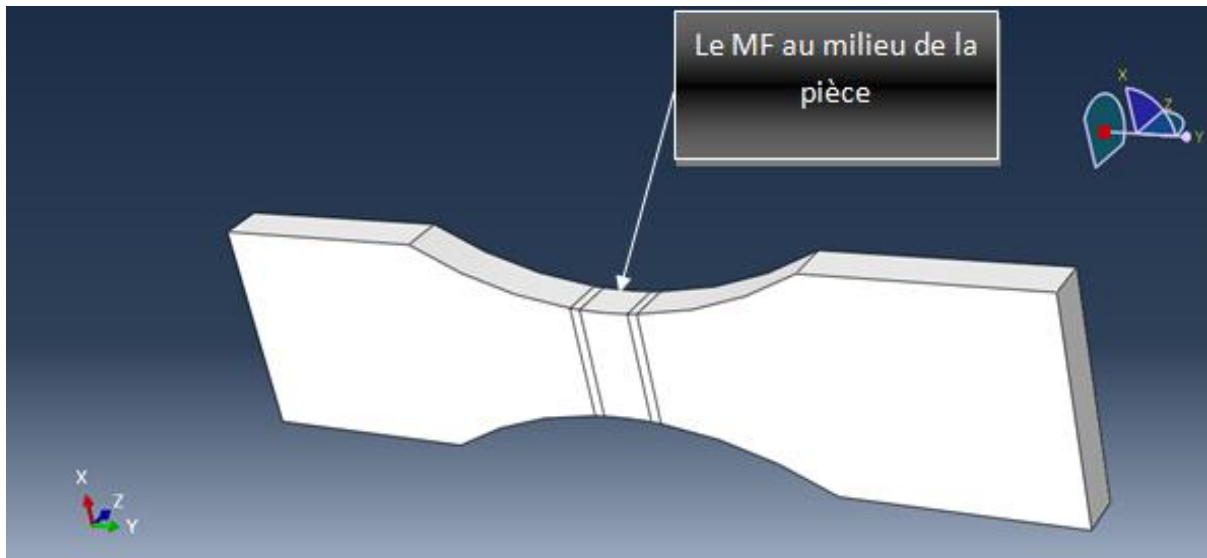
modèle géométrique de l'éprouvette soudée
